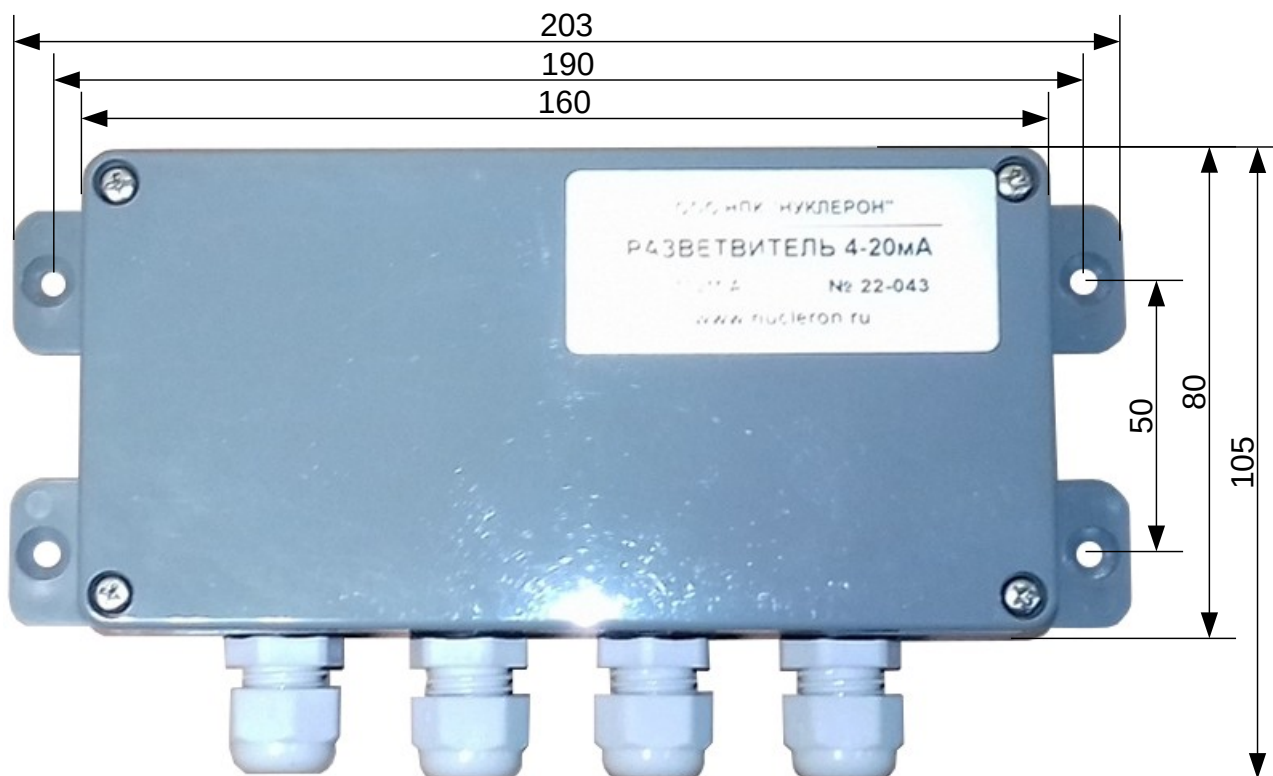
Габаритные размеры разветвителя NUC-102M-A
